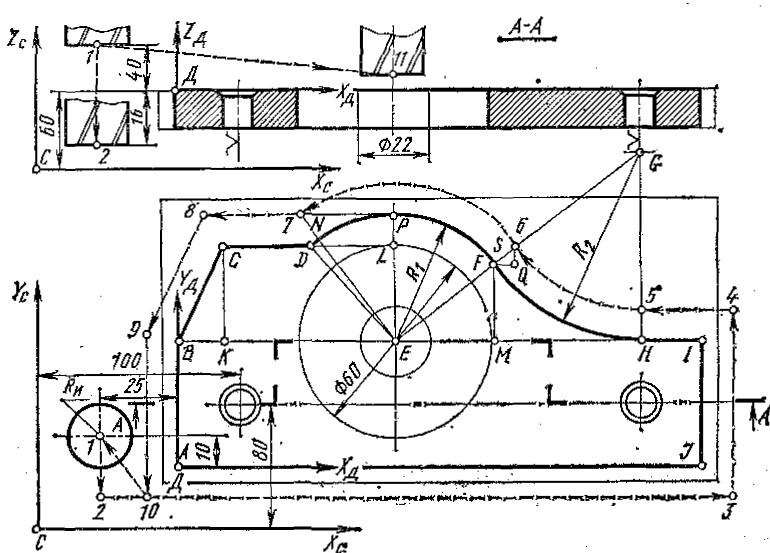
Операционный эскиз фрезерной обработки детали «крышка»
